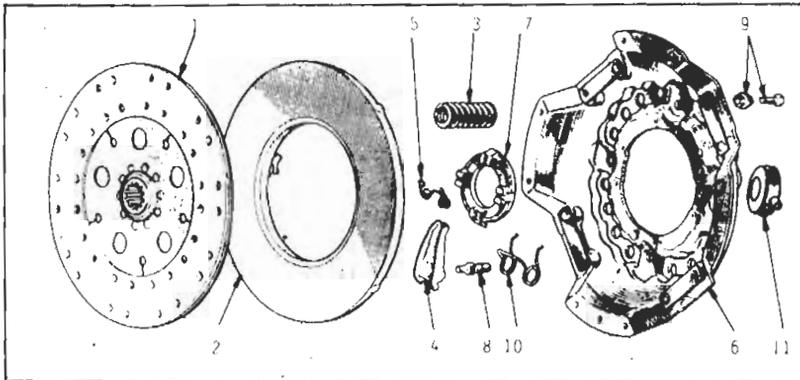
Despiece de un embrague de disco. 1.- Disco. 2.- Plato de presión. 3.- Muelles. 4.- Patilla. 5.- Muelle de las patillas. 6.- Campana. 7.- Anillo tope de las patillas. 8.- Tornillo reglaje de las patillas. 9.- Tornillos sujeción de la campana. 10.- Muelle del collarín. 11.- Collarín.
